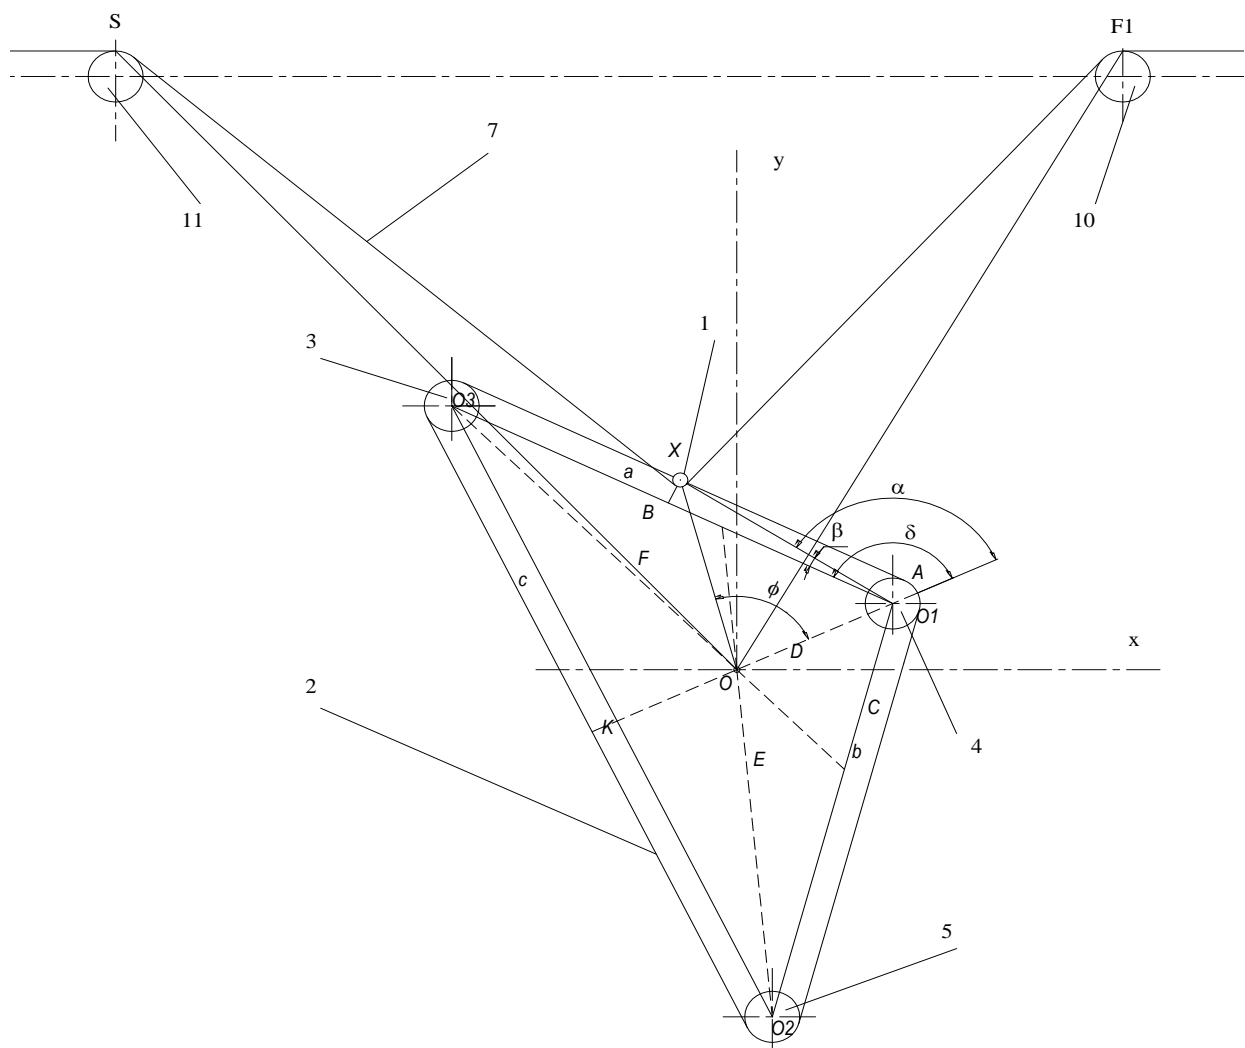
Розрахункова схема механізму компенсації уточної нитки з трьома зубчастими колесами
